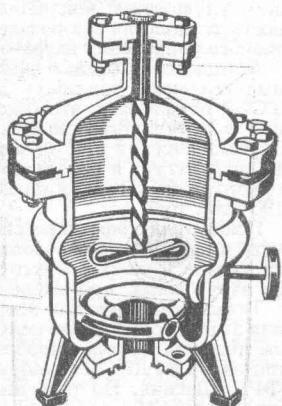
Макет химического аппарата, изготовленного с использованием способа диффузионной сварки в вакууме (плакировка внутренней поверхности аппарата медной или серебряной фольгой).
